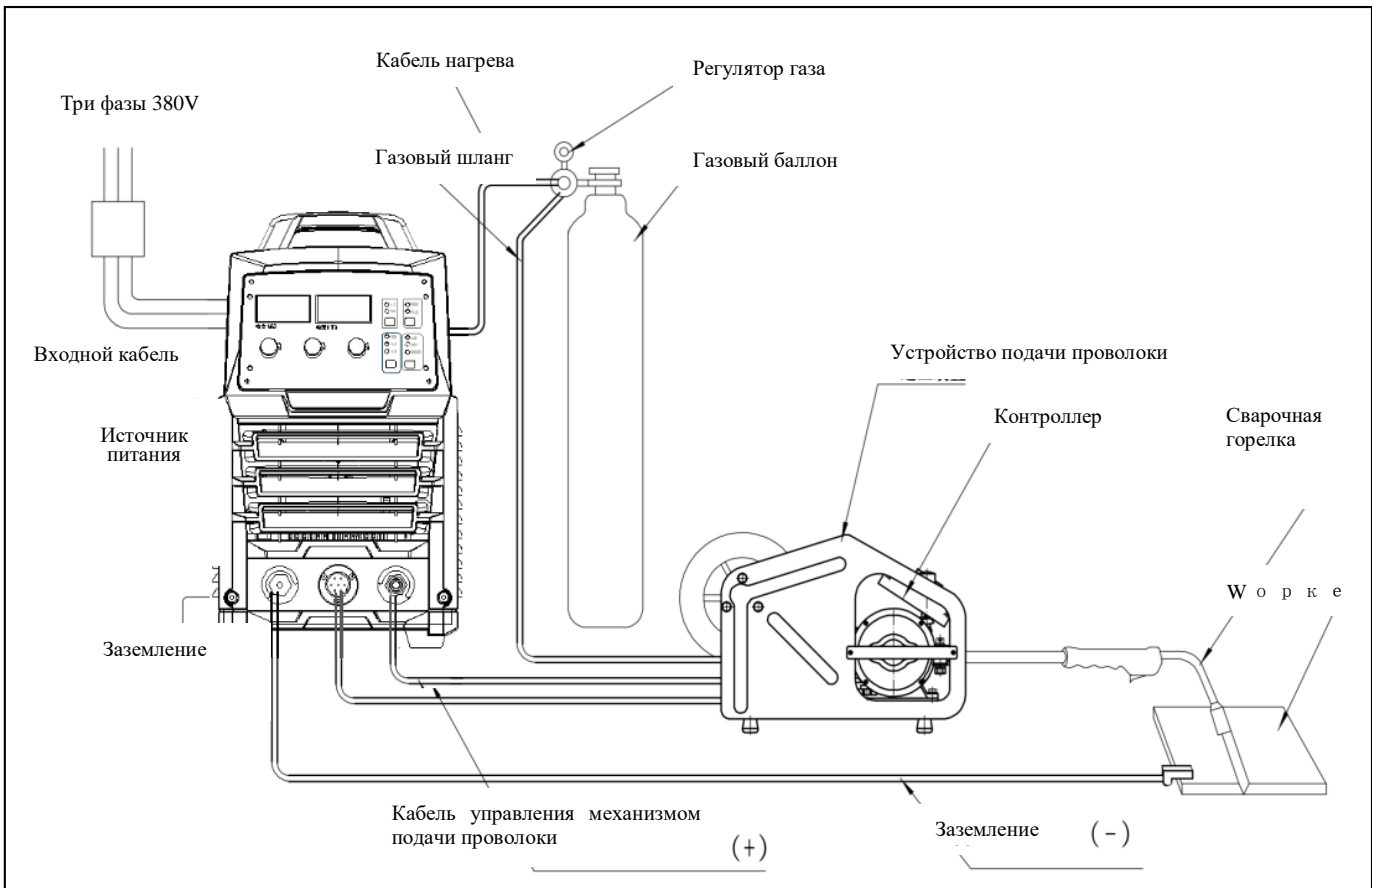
Схема подключения и сборки источника сварочного аппарата и подающего механизма.
